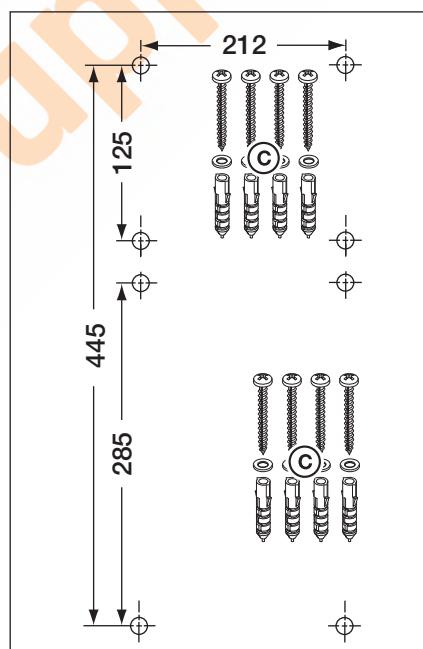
Bohrbild der Befestigungslöcher, benötigtes Montagematerial
